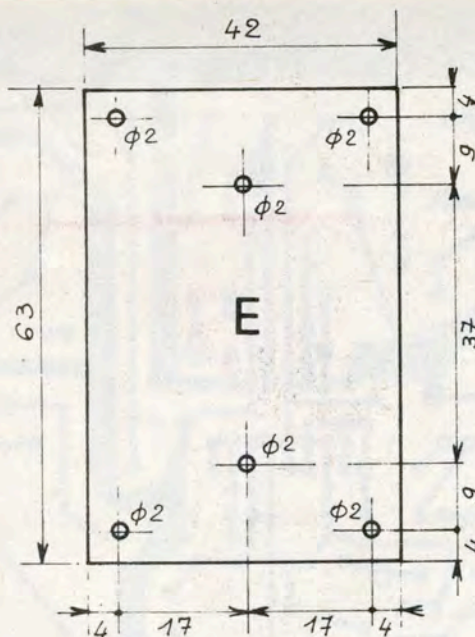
Flaque arrière du transfo THT. Epoxy Cu.
